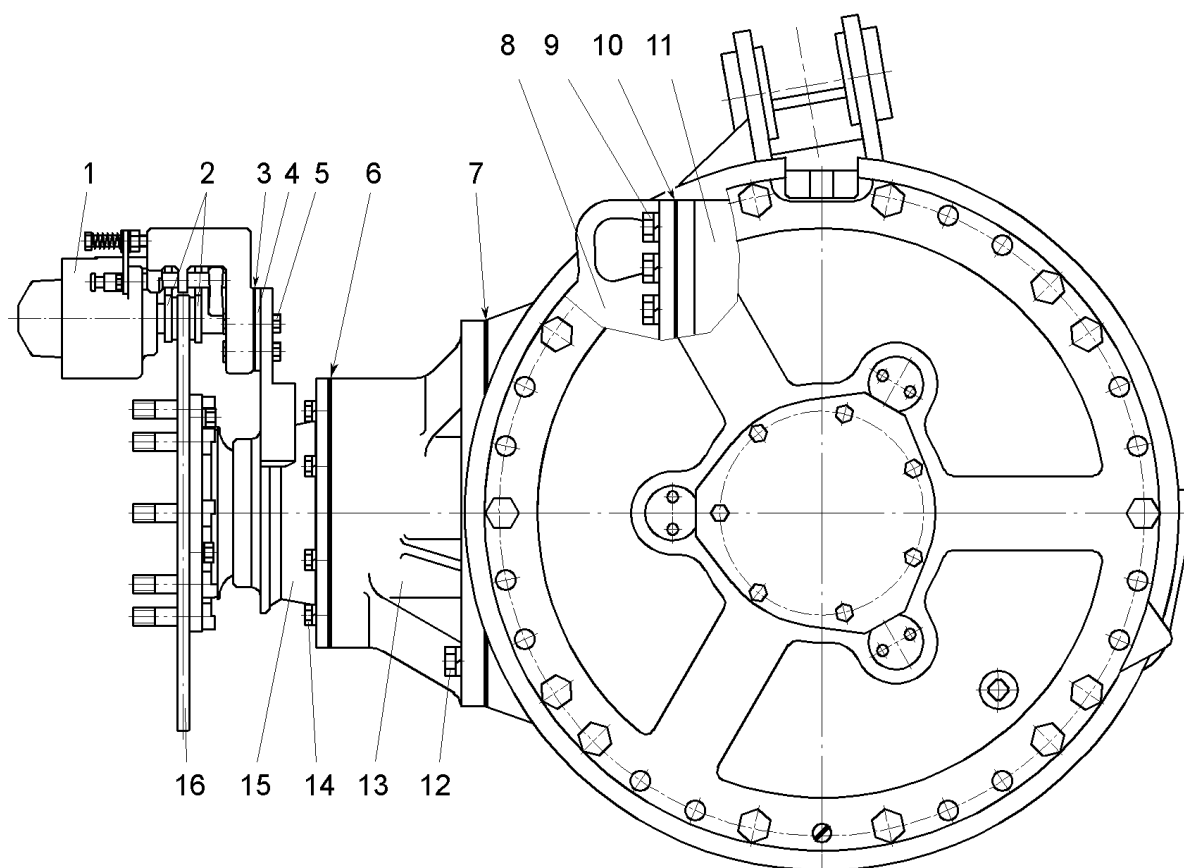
Установка главной передачи и стояночного тормозного механизма:
